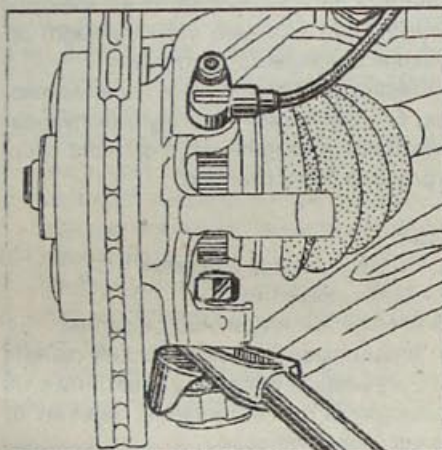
Использование ударного съемника для выпрессовки нижнего шарового шарнира
